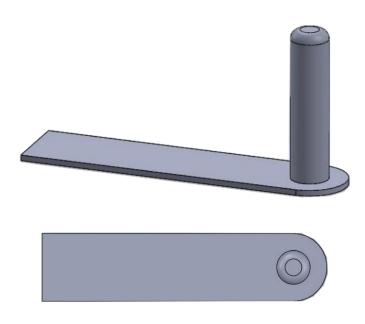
Detalle empuñadura Fuente: Elaboración Propia
